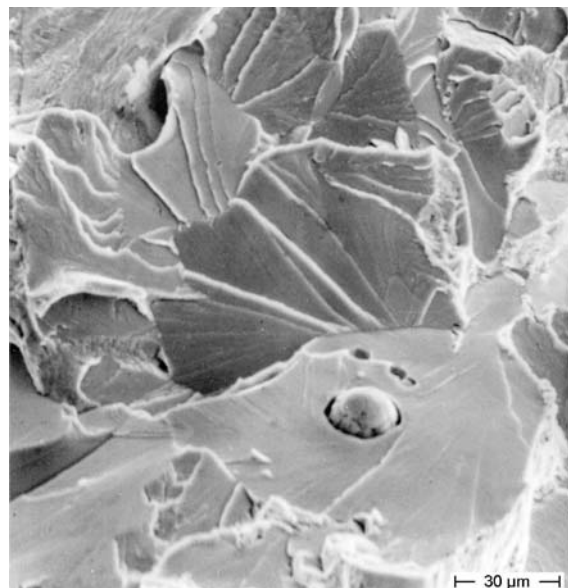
Restgewaltbruch; Einschluss beim Spalten angeschnitten
